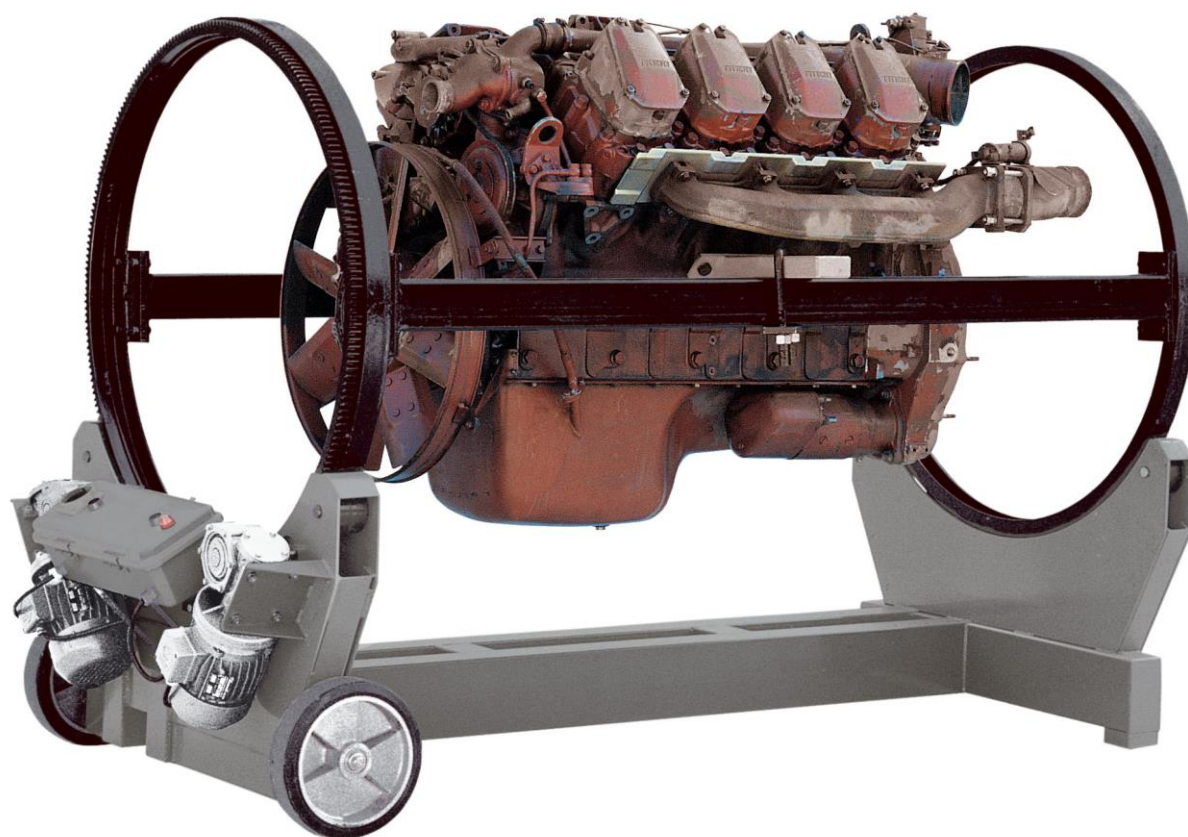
Стенд разборки—сборки двигателей R15
